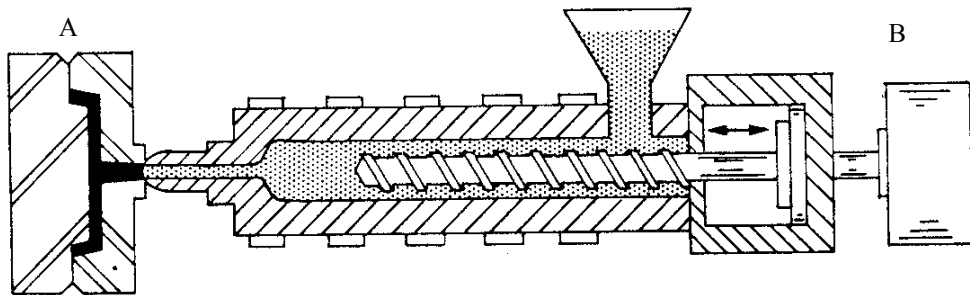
Esquema de uma máquina de injeção de polímeros: A – molde; B – motor
